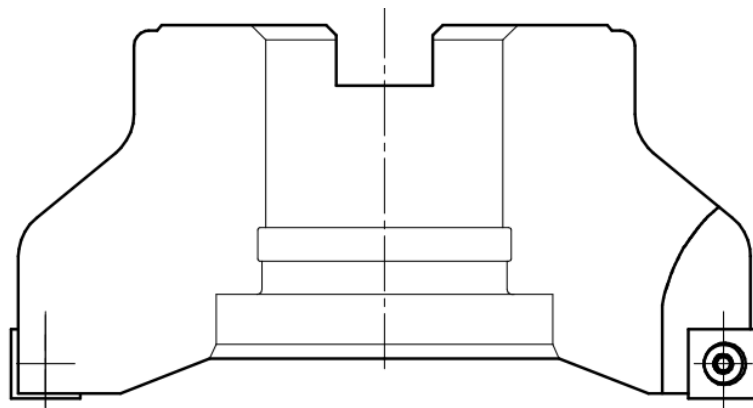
Фреза торцева зі змінними пластинами
